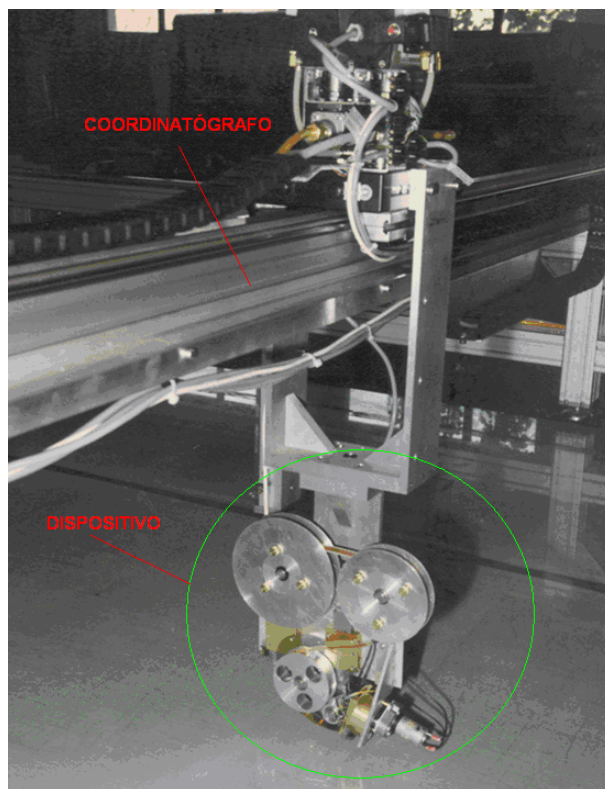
Dispositivo para el posicionado y dispensado de electrodos
